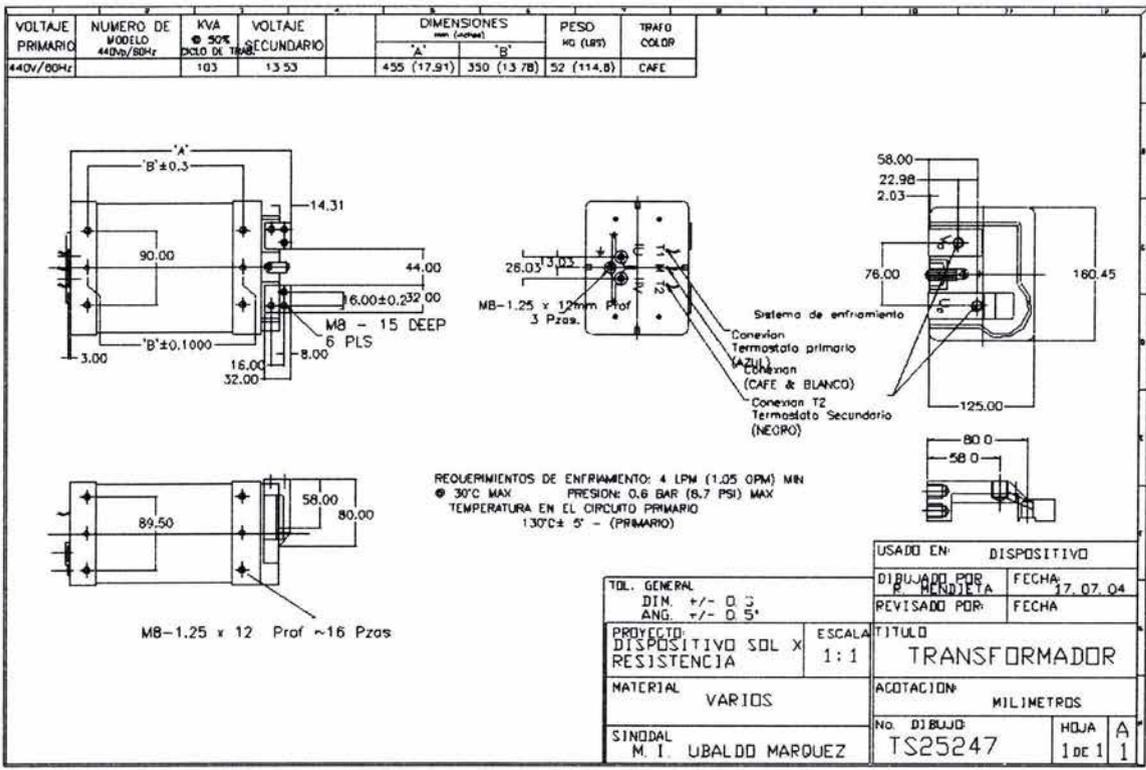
Transformador de soldadura que proporcionara la corriente de soldadura necesaria para el proceso.
